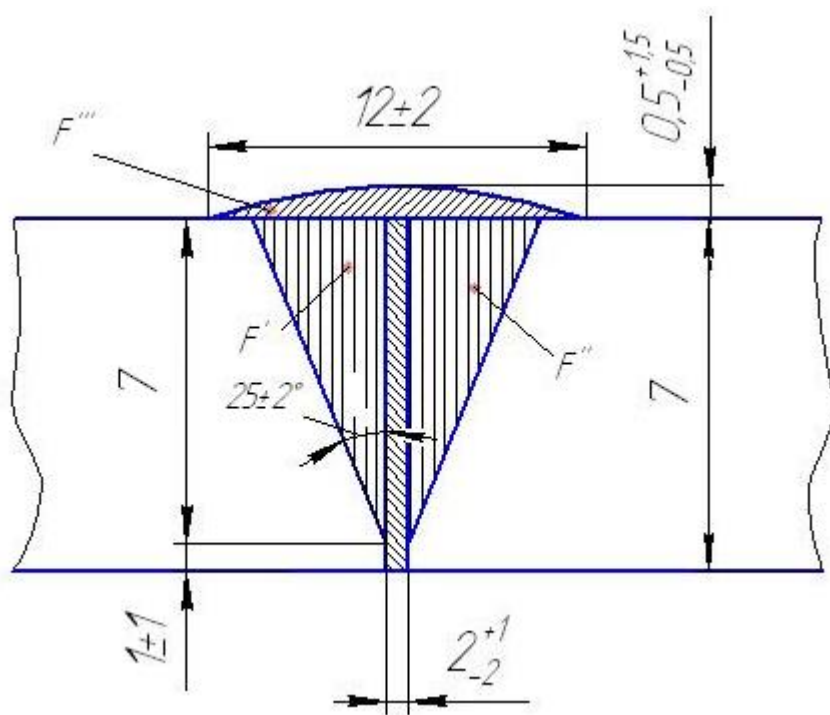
При ручной дуговой сварке покрытыми электродами геометрические элементы площади сечения стыкового шва
